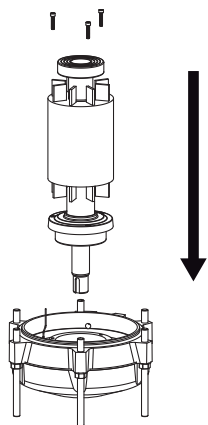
Монтаж шарикоподшипника (J 205, J 405)
